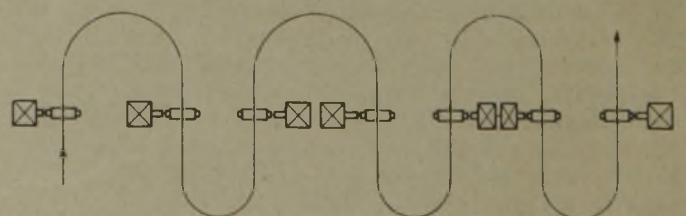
Drahtwalzwerk mit nebeneinander angeordneten, einzeln angetriebenen Walzgerüsten.
